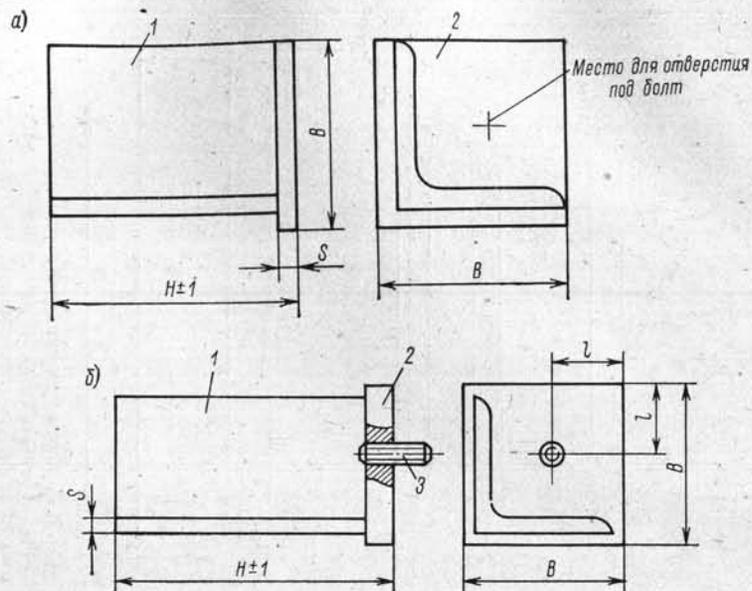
Стойки приварные: а — для помещений без зашивки изоляции; б — для помещений с зашивкой изоляции.
